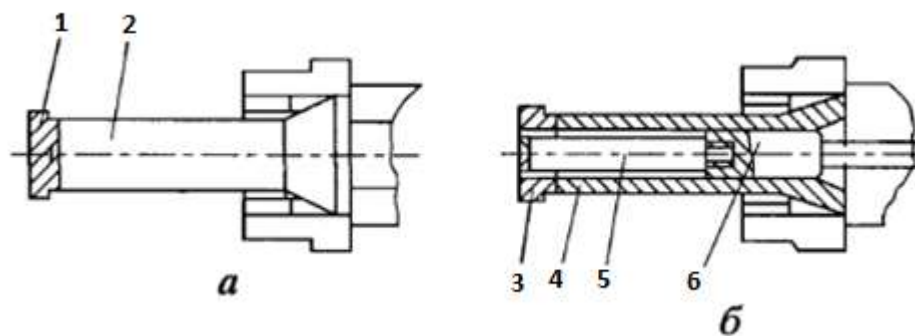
Конструкция инструмента: а – для прессования профилей; б – для прессования труб: 1 – пресс-шайба; 2 – пресс-штемпель; 3 – полая пресс-шайба; 4 – полый пресс-штемпель; 5 – прошивная игла; 6 – вал
